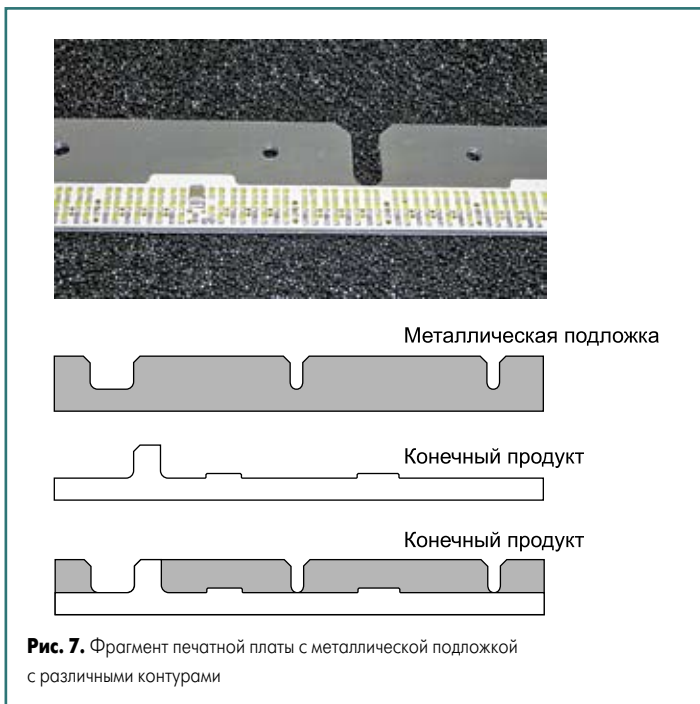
Фрагмент печатной платы с металлической подложкой с различными контурами
